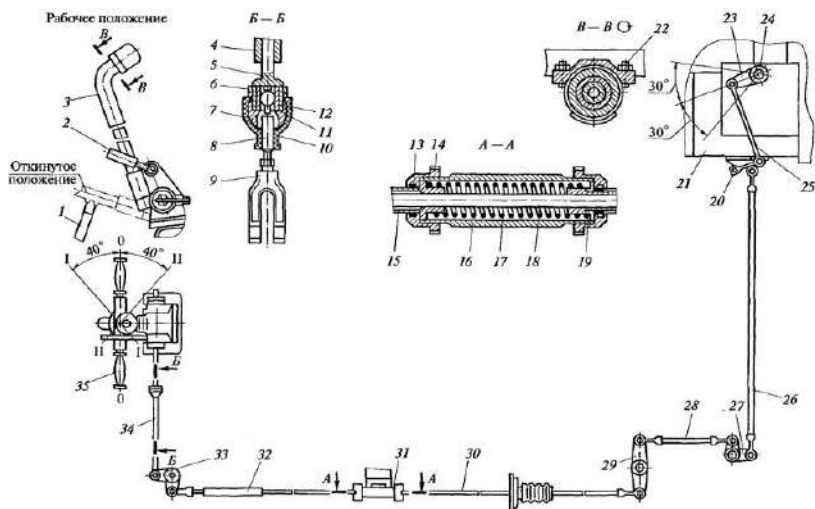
Привід керування ГОМП: 1 – упор; 2 – рукоятка стопора; 3 – рульова колонка; 4 – втулка картера; 5 – зубчаста рейка; 6, 7, 14 – гайки; 8 – палець; 9 – вилка; 10 – чохол; 11, 12 – вкладиші; 13 – ущільнювальне кільце; 15, 19 – втулки; 16 – корпус; 17 – пружина; 18 – шток; 20 – вертикальний валик; 21 – гідропривід; 22 – упорні гвинти; 23, 27, 29, 33 – важелі; 24 – валик; 25 – регульована тяга; 26, 28, 30, 32, 34 – тяги; 31 – нуль-установник; 35 – штурвал; О, І, ІІ – положення штурвала
